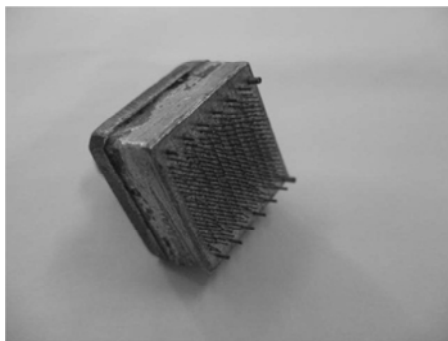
Общий вид многоместного инструмента для прошивания отверстий
